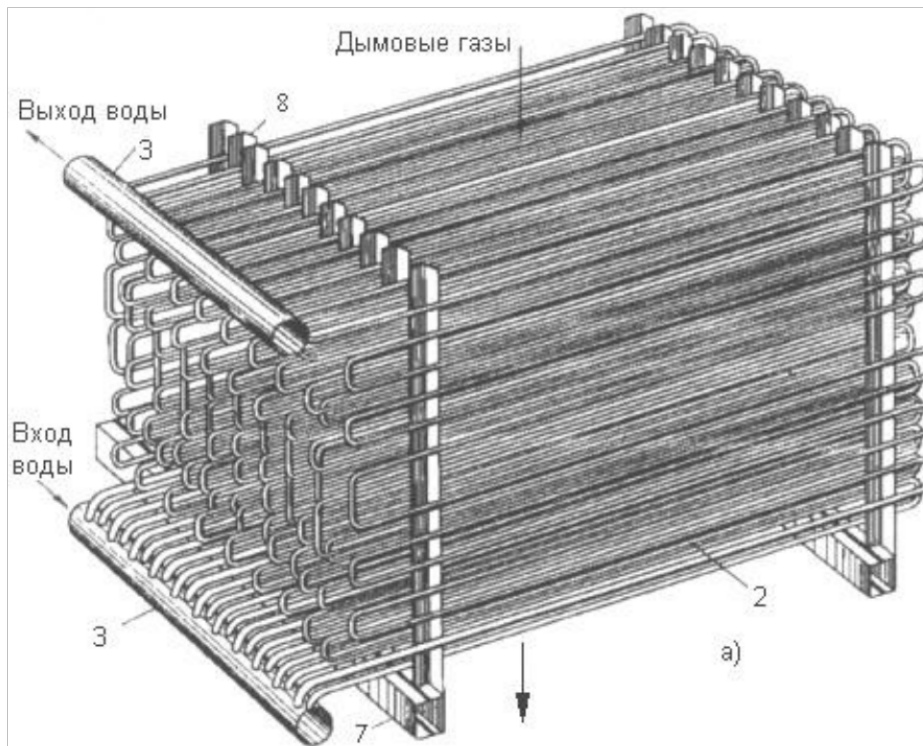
а Общий вид пакета экономайзера: 2 - трубные змеевики; 3 - коллектор; 7 - опорная балка; 8 - опорные стойки.
